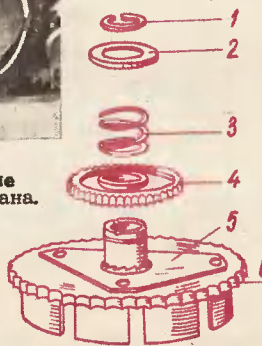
Разборка большого барабана: 1 — стопорное кольцо; 2 — упорная шайба; 3 — пружина; 4 — заводная шестерня; 5 — поводок с зубьями; 6 — барабан со звездочкой.
